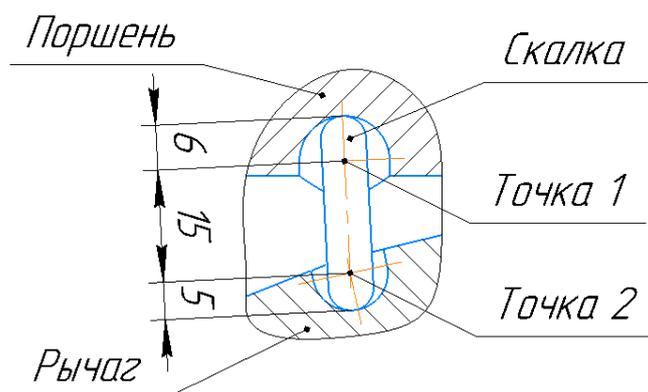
Схема сопряжения рычага и поршня со скалкой
